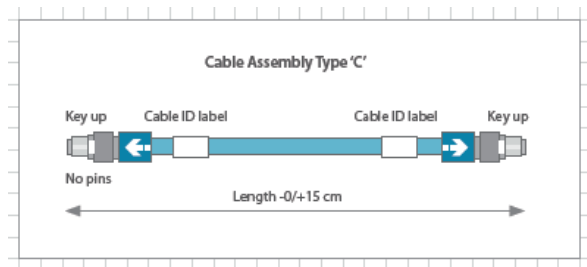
Cabo de inter-ligação tipo "C" do sistema MT Connect
